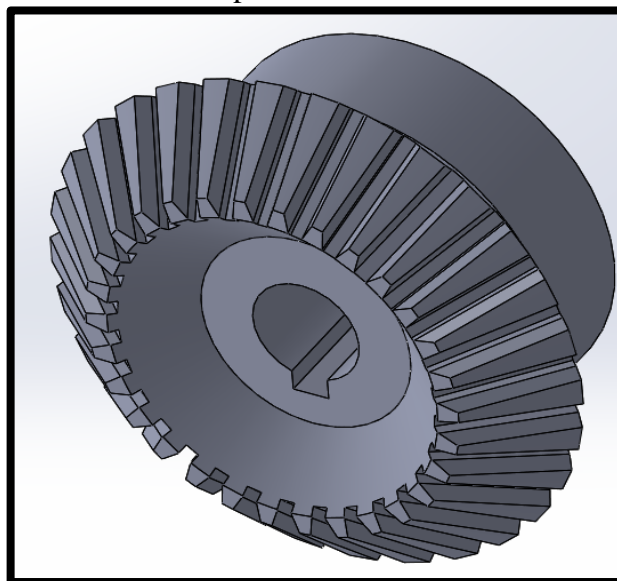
Detalle del chavetero del engranaje cónico recto, una vez mecanizados. Fuente: Propia.
